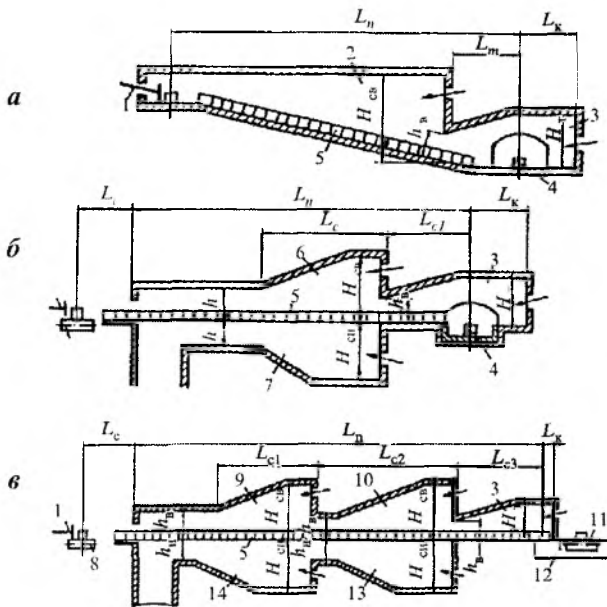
Методические нагревательные печи: а — с двумя верхними отсеками горения (боковая загрузка и выгрузка); б — с двумя верхними и одним нижним отсеками горения (торцевая загрузка и боковая выгрузка); в — с пятью отсеками горения (три верхних и два нижних, торцевая загрузка и торцевая выгрузка); 1 — толкатель; 2 — сварочная зона; 3 — томильная зона (зона выдержки); 4 — окно выдачи; 5 — нагреваемая садка; 6, 10 — верхний отсек сварочной зоны; 7, 13 — нижний отсек сварочной зоны; 8 — рольганг загрузки; 9 — верхний отсек методической зоны; 11 — рольганг выдачи; 12 — штанги машины выдачи; 13 — нижний отсек сварочной зоны; 14 — нижний отсек методической зоны
